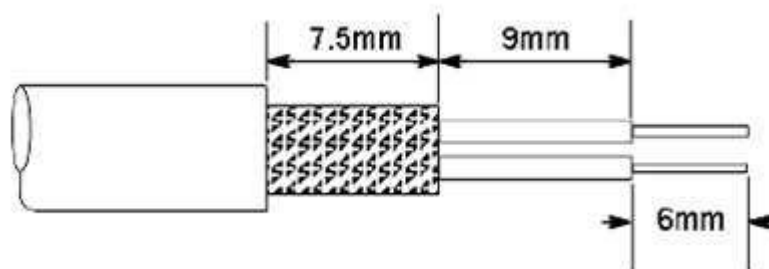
Detalhe da Preparação do Cabo PROFIBUS
